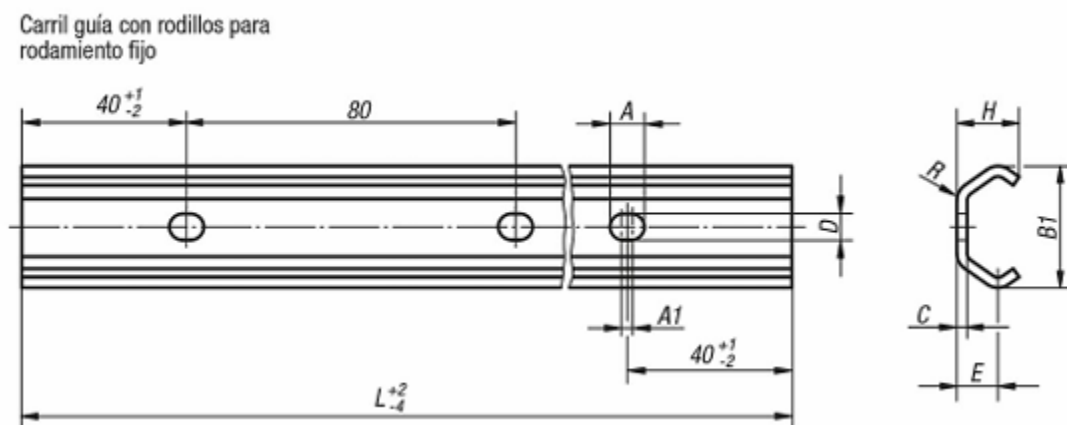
Vista frontal y lateral izquierda de un carril guía Norelem.
